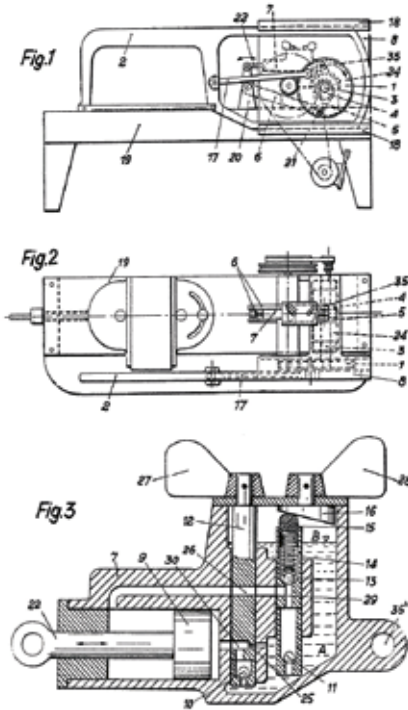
Bei dieser Bügelsägemaschine wird mit einer Kolbenstange ein Sägebügel durch einen Exzenter an der Kurbelscheibe so über das Werkstück geführt, dass er erst bei Rückführung schneidet
